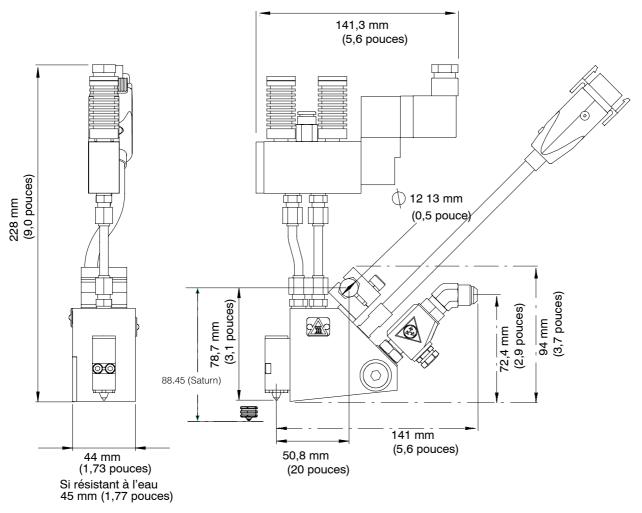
Dimensions d'un pistolet mono-module configurable à électrovanne SG
